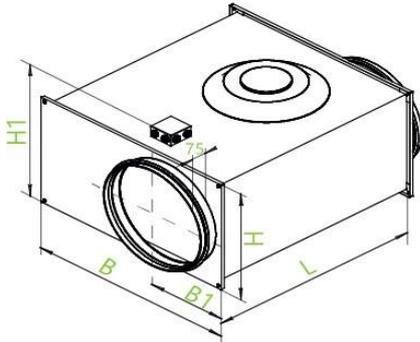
Габаритные установочные и присоединительные размеры вентиляторов
